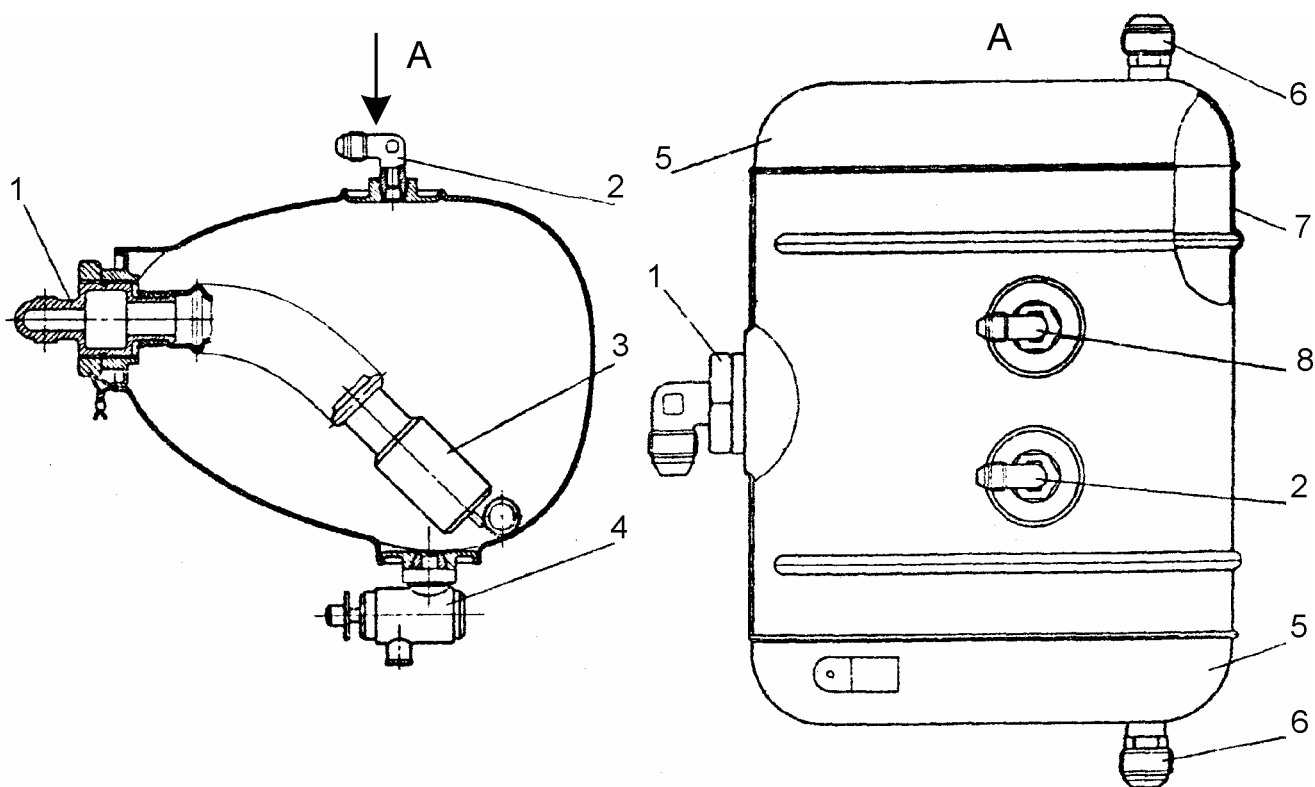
Фюзеляжний жорсткий бак (витратний бак Як-55):
